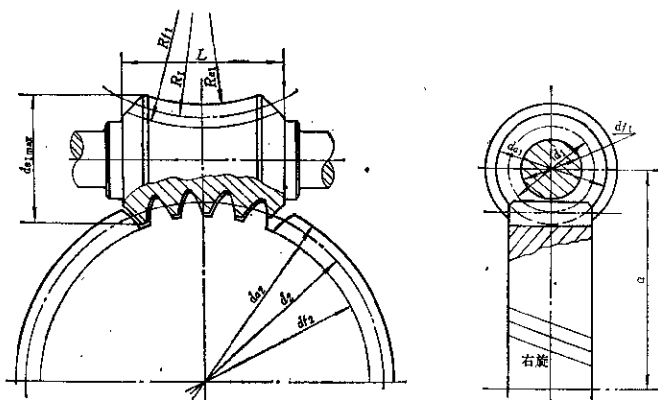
渐开线圆柱齿轮-环面蜗杆传动几何尺寸
